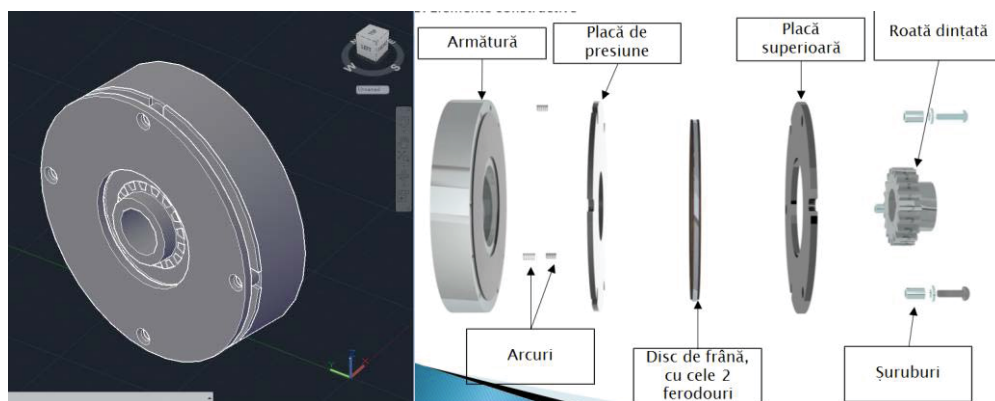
Modelul geometric AutoCAD 3D și o vedere explodată a elementelor componente
